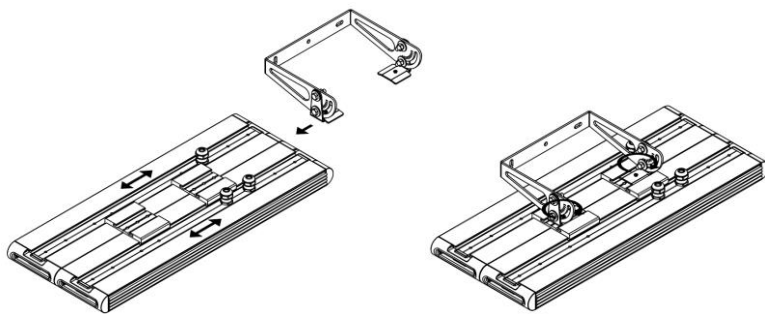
Установка крепления на соединительные планки на примере светильника Element 0,5x2 и Крепления Скоба малая с регулировкой.
